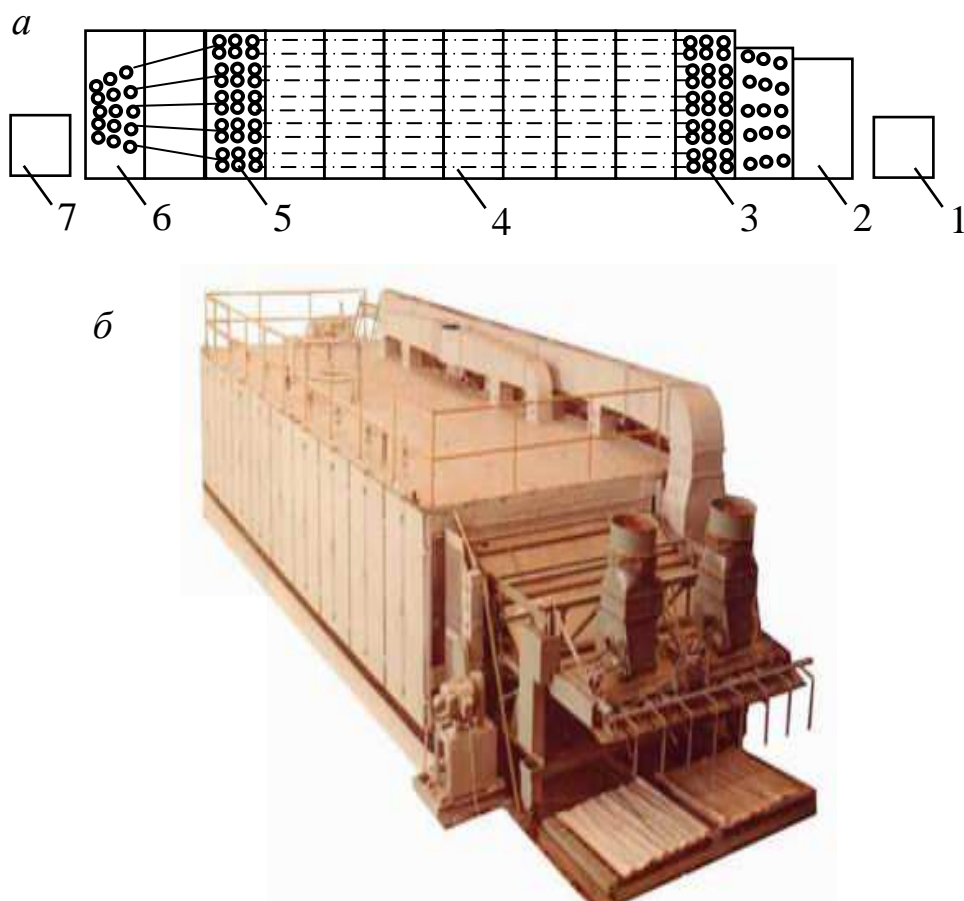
Роликовая сушилка: *а* – схема; *б* – общий вид
